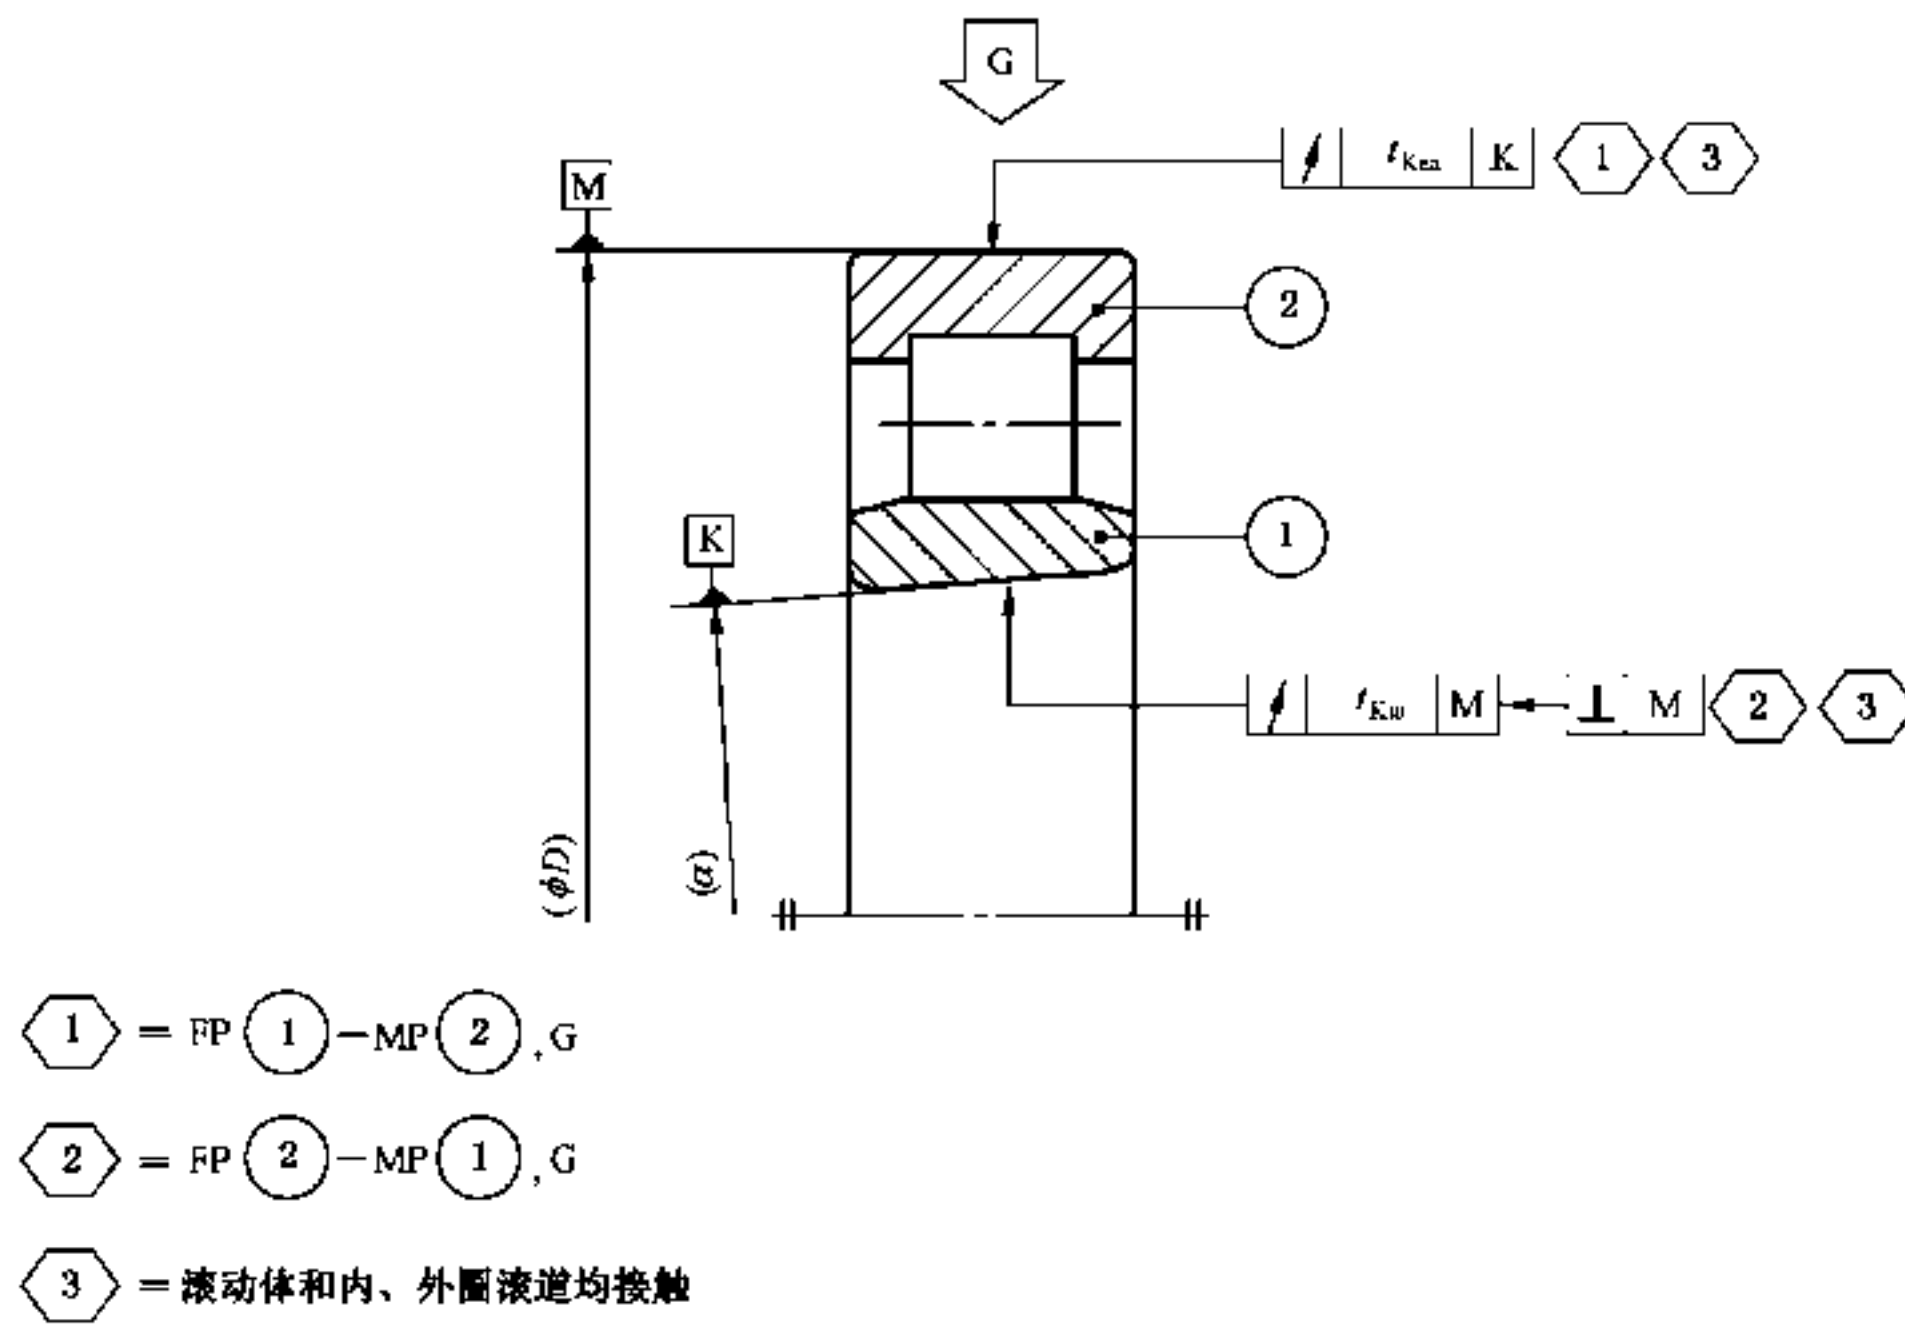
圆锥孔成套轴承的几何公差——圆柱滚子轴承、调心滚子轴承、长弧面滚子轴承和调心球轴承
